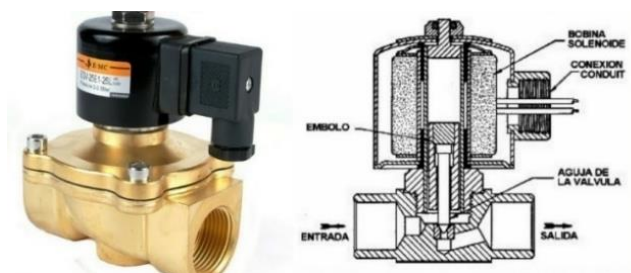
Actuador – Electroválvula, (a) vista isométrica, (b) corte total del actuador para identificar sus componentes [37]
